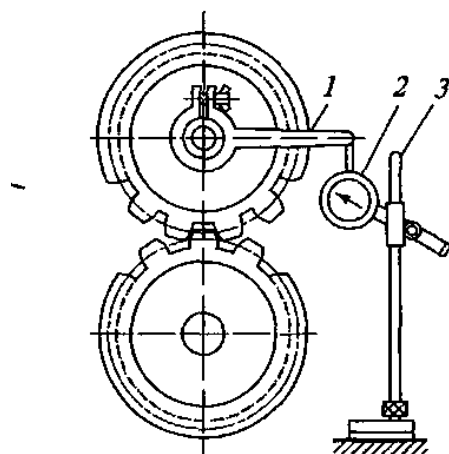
Індикаторний пристрій для виміру бокового зазору між зубцями: 1 – поводок; 2 – індикатор; 3 – стійка.
